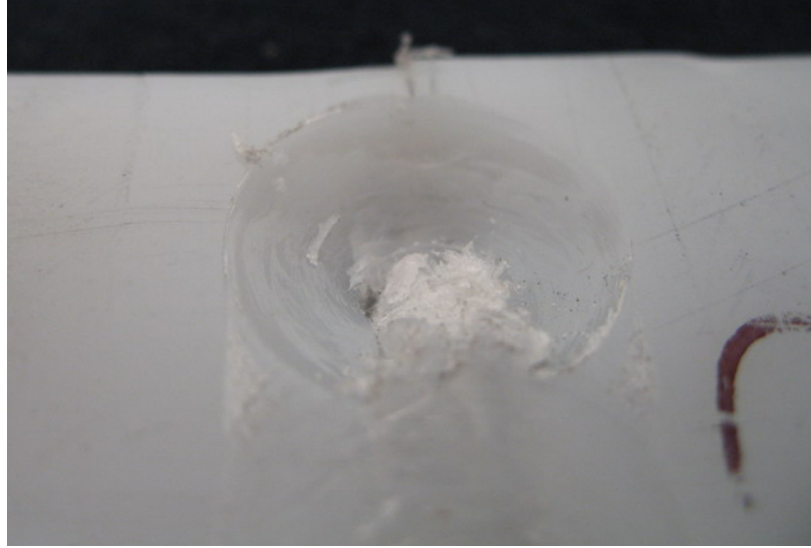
'da kaynaklı bölgenin bir tarafında malzeme yığılması olduğu görülmektedir. Bu durumun, takım omzunun parça yüzeyine çok aşırı bastırıldığı durumlarda meydana geldiği gözlemlenmiştir. Omuz parça yüzeyine fazla bastırıldığı zaman, parçaya dalarak oymaya başlar ve dönüş esnasında çıkardığı malzemeyi kaynak bölgesi kenarına yığarak çapak oluşturur. Bu çapak oluşan bölge, Şekil 2.18'de gösterilen kaynağın geri çekilen kısmında meydana gelir. Bu da kaynak bölgesinde malzeme kaybı ve mukavemette düşüşe sebep verir. Bu nedenle takım omzunun malzeme üzerine yapacağı baskı iyi ayarlanmalıdır.
